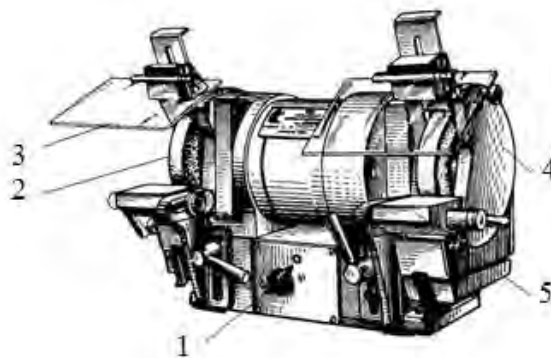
Точильно-шлифовальный двухсторонний станок ЗК631-01
